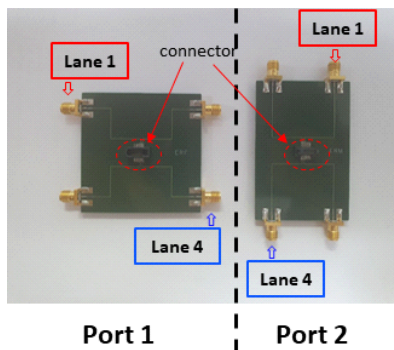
측정을 위해 커넥터와 PCB 보드를 납땜한 모습
